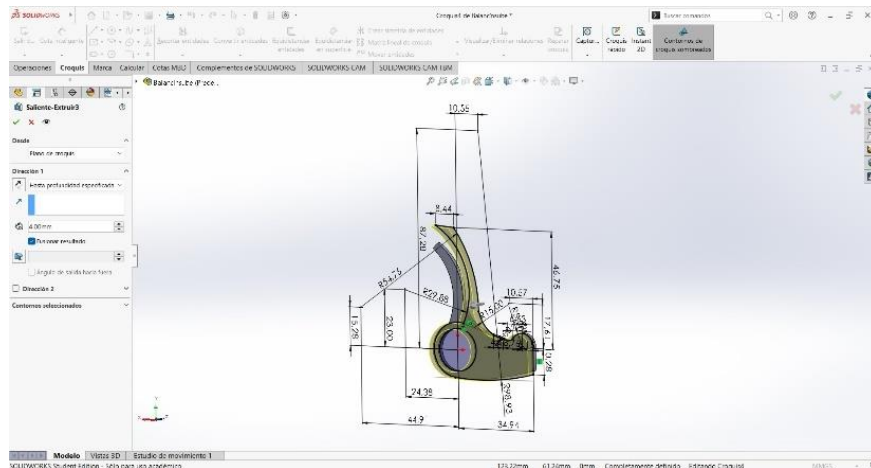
Balancín 1 (Extrusionado de Croquis 3). Fuente: SolidWorks
